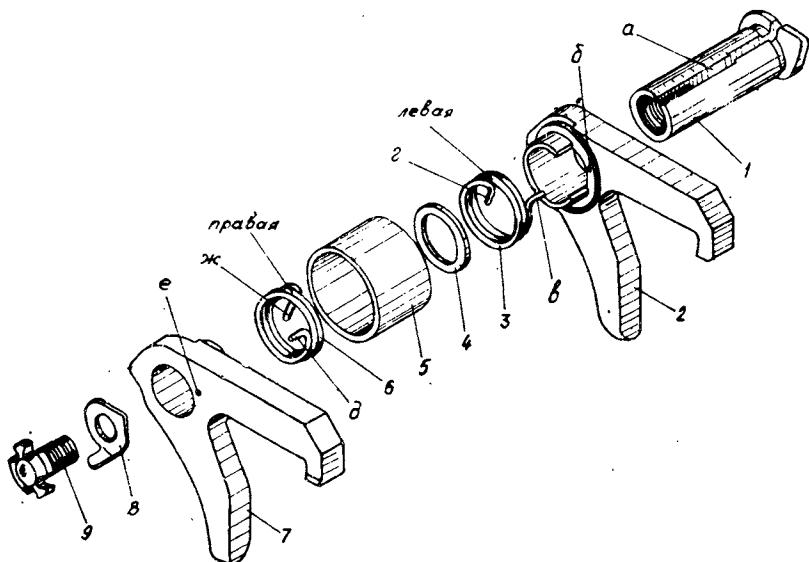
Установка пружин предохранительного механизма 04-2 Сп:
